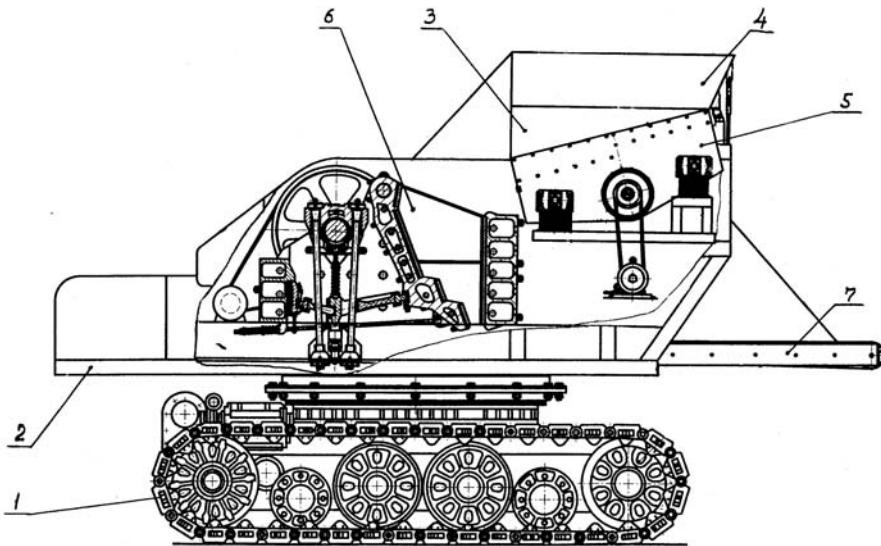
Конструктивная схема самоходной дробильной установки: 1 – гусеничное ходовое оборудование; 2 – платформа; 3 – приемный бункер; 4 - откидывающиеся боковины бункера; 5 – виброгрохот-питатель; 6 – щековая дробилка со ступенчатой камерой дробления; 7 – поворотный ленточный конвейер
